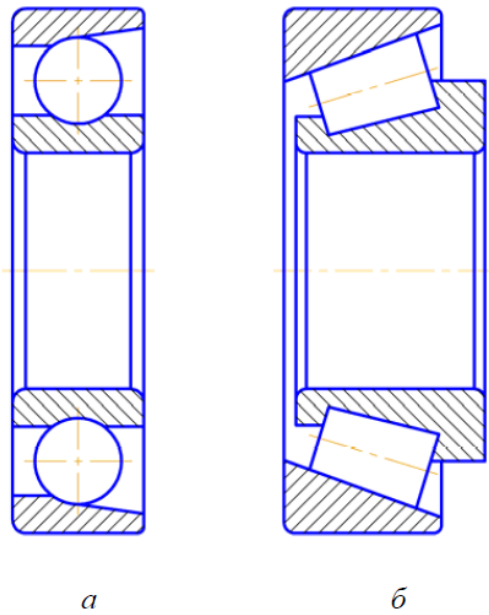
Упорно-радіальні підшипники кочення
